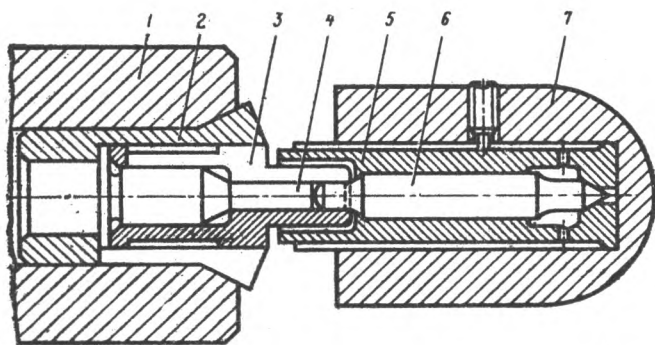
Приспособление для восстановления конусов в распылителе новой конструкции:
